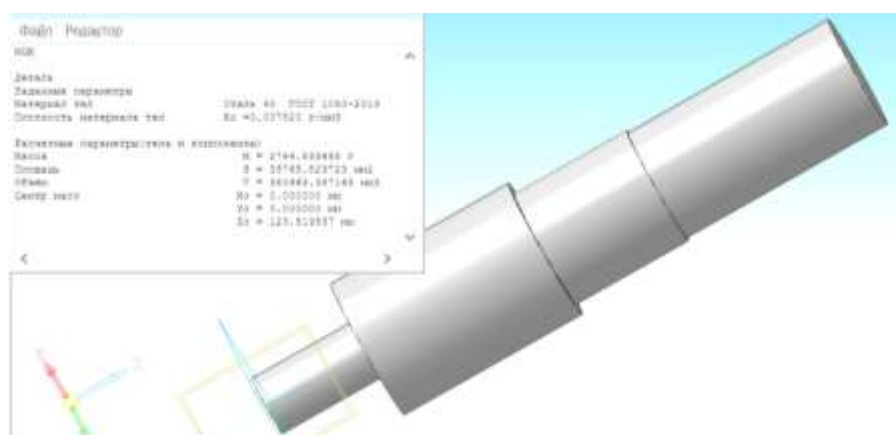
Заготовка отримана штампуванням на КГШП
